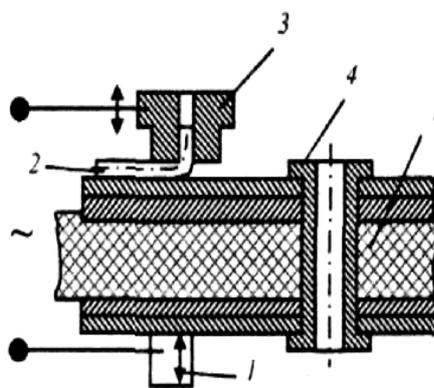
Схема сварки монтажных проводов (1, 3 – электроды, 2 – провод, 4 – монтажная площадка, 5 – плата)
